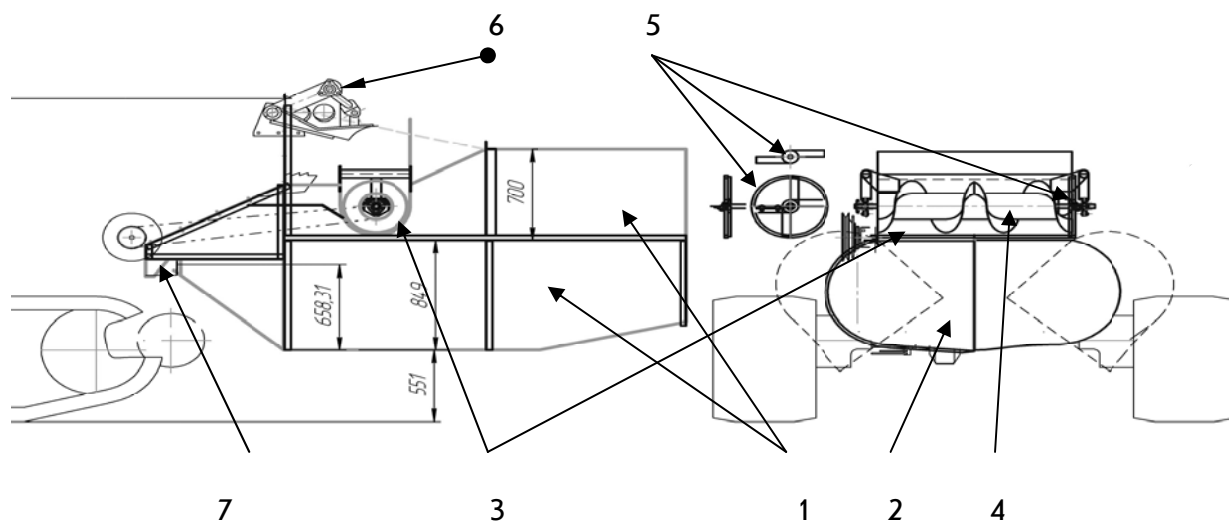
Копнитель-половосборник (вид сбоку, вид сзади):
